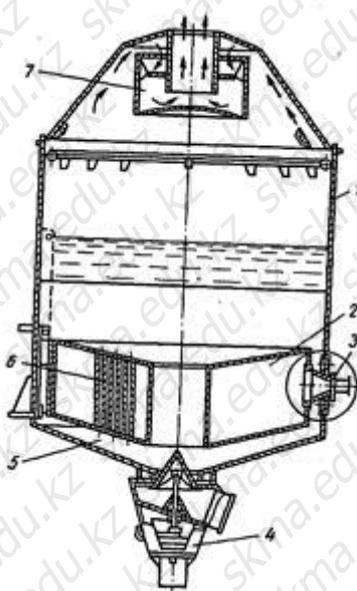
Вакуум-аппарат с подвесной греющей камерой: 1 — корпус; 2 — греющая камера; 3 — устройство для ввода пара; 4 — циркуляционная труба; 5 — днище; 6 — греющая труба; 7 — сепаратор инерционного типа
